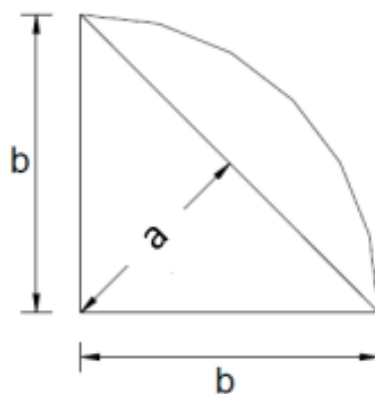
Legenda da secção transversal do cordão de soldadura (Retirado de: Fonseca, 2022).
